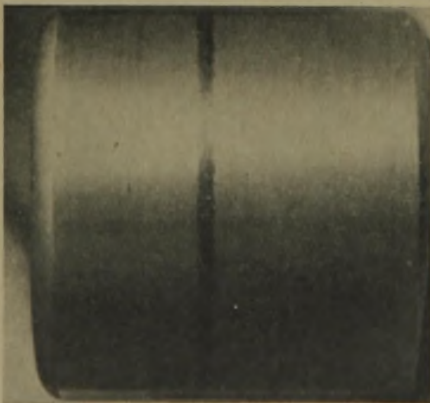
Freßspuren auf dem Mantel einer Zylinderrolle
